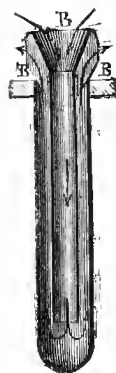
Tube de la chaudière du moteur fixe de MM. Leccointe et Villette.
